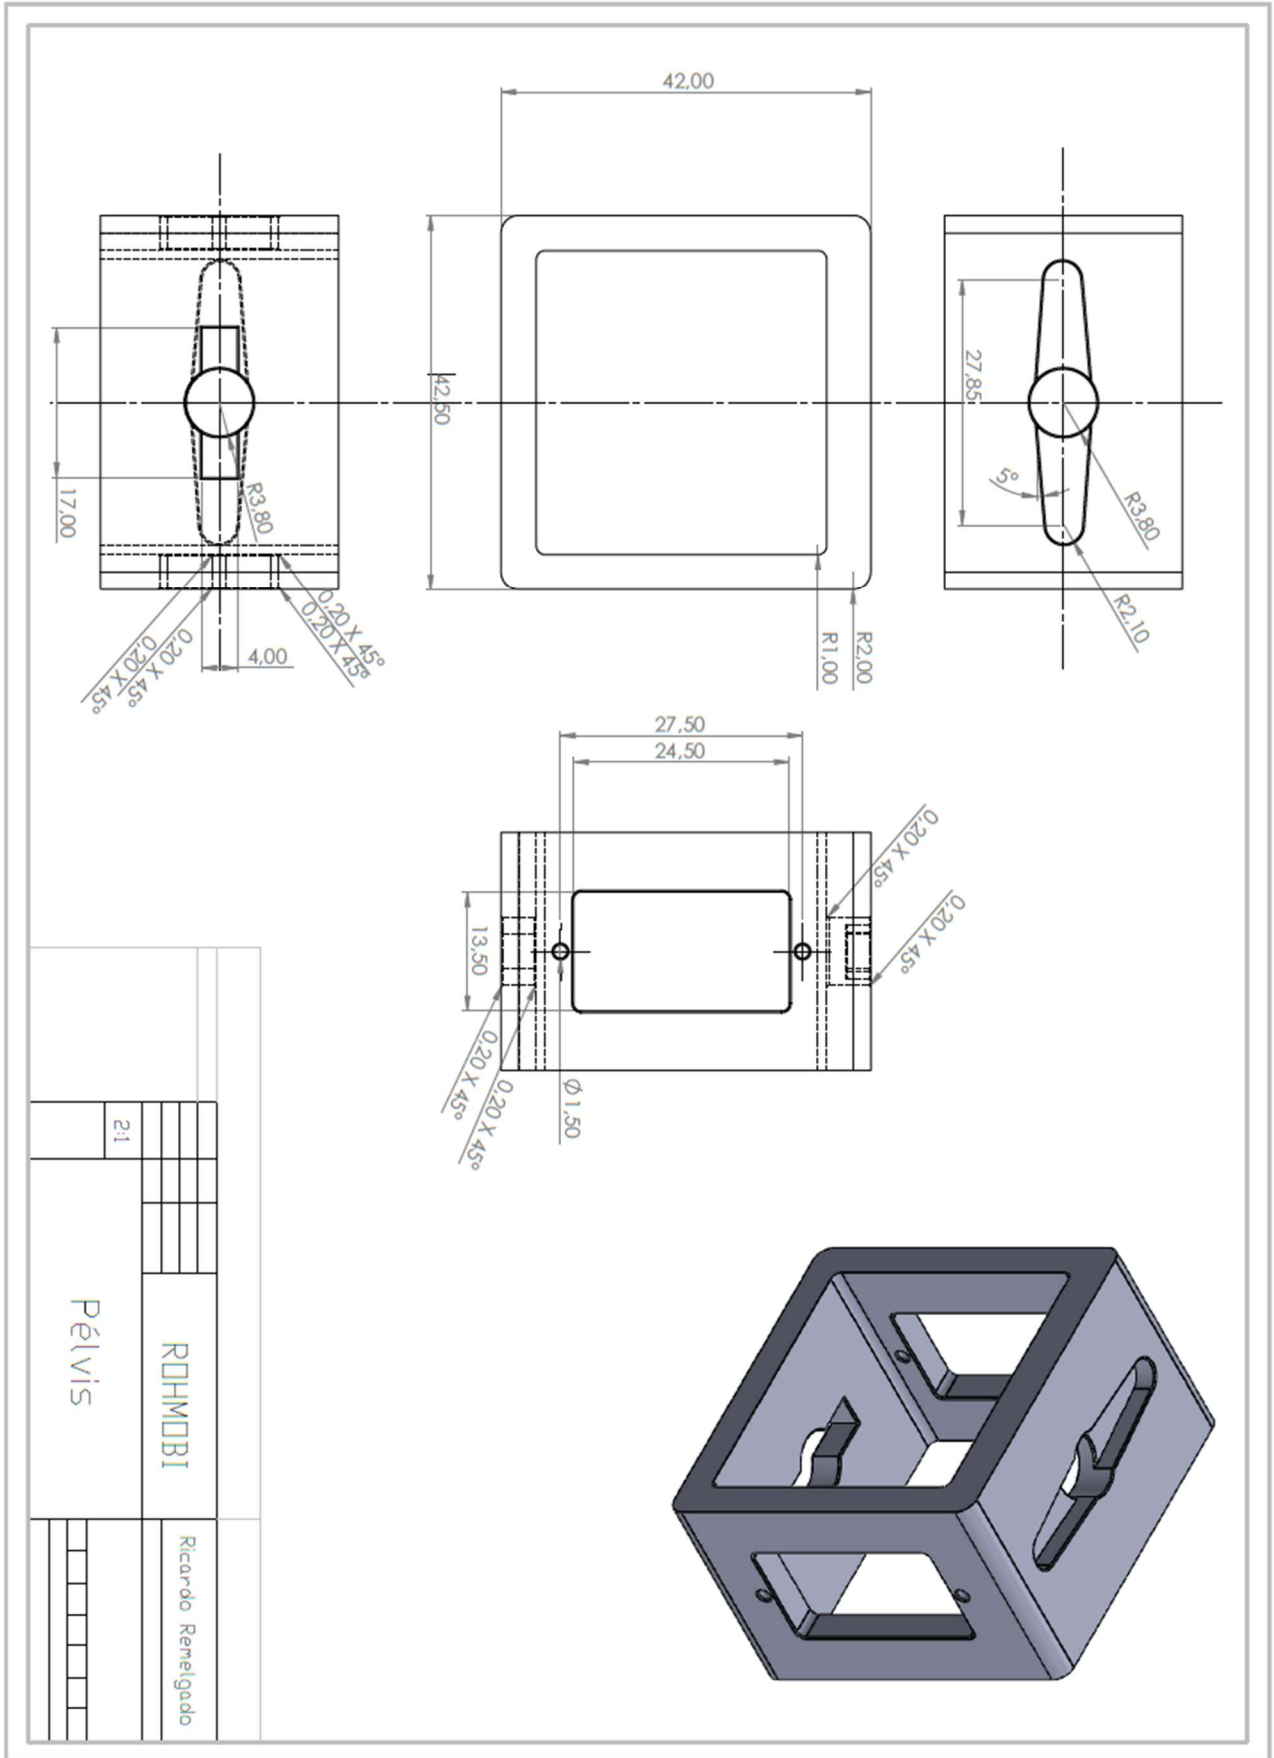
Desenho técnico da pélvis do ROHMOBI
